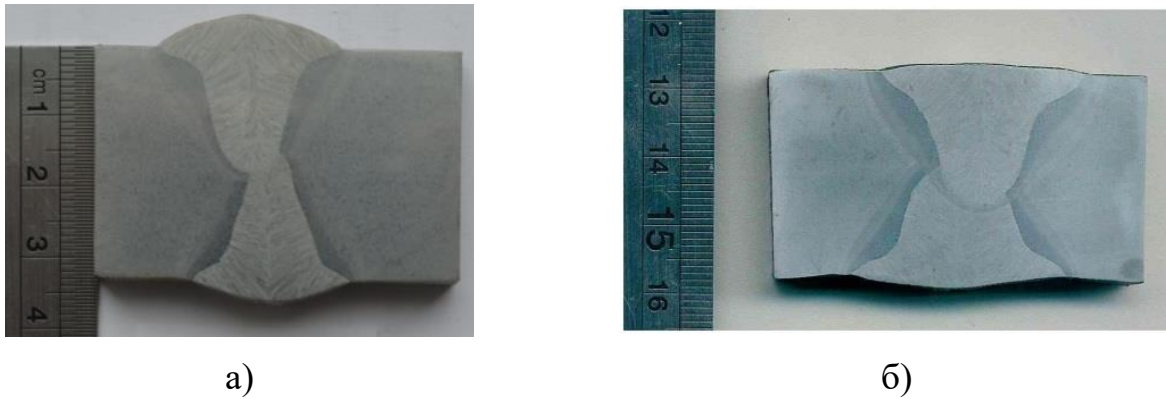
Поперечное сечение сварных швов труб типоразмером 1220х30,9 мм:
